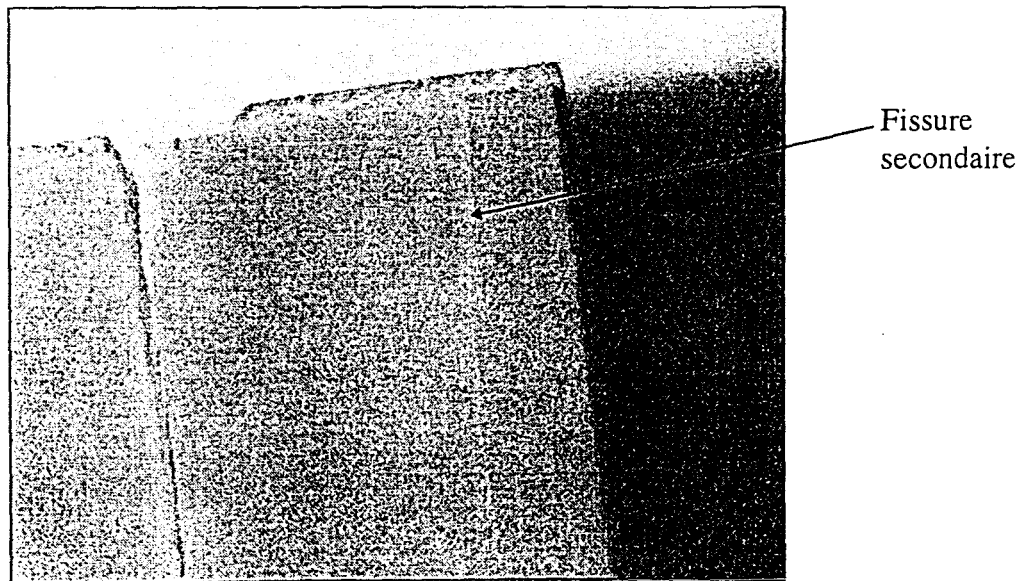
exemple de fissuration en dehors de la zone utile
